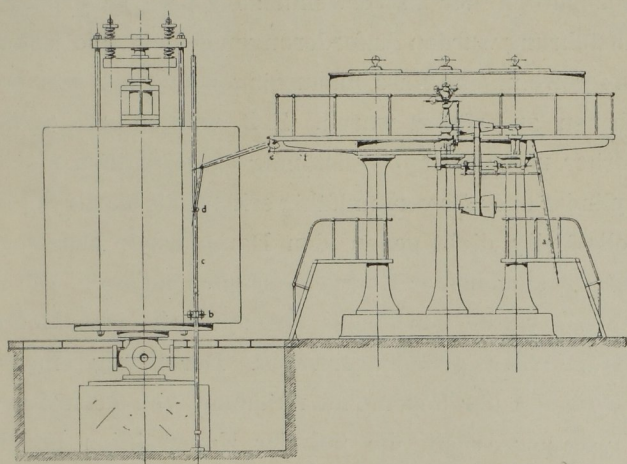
Ansicht der Pumpmaschine und des Kraftsammlers.
